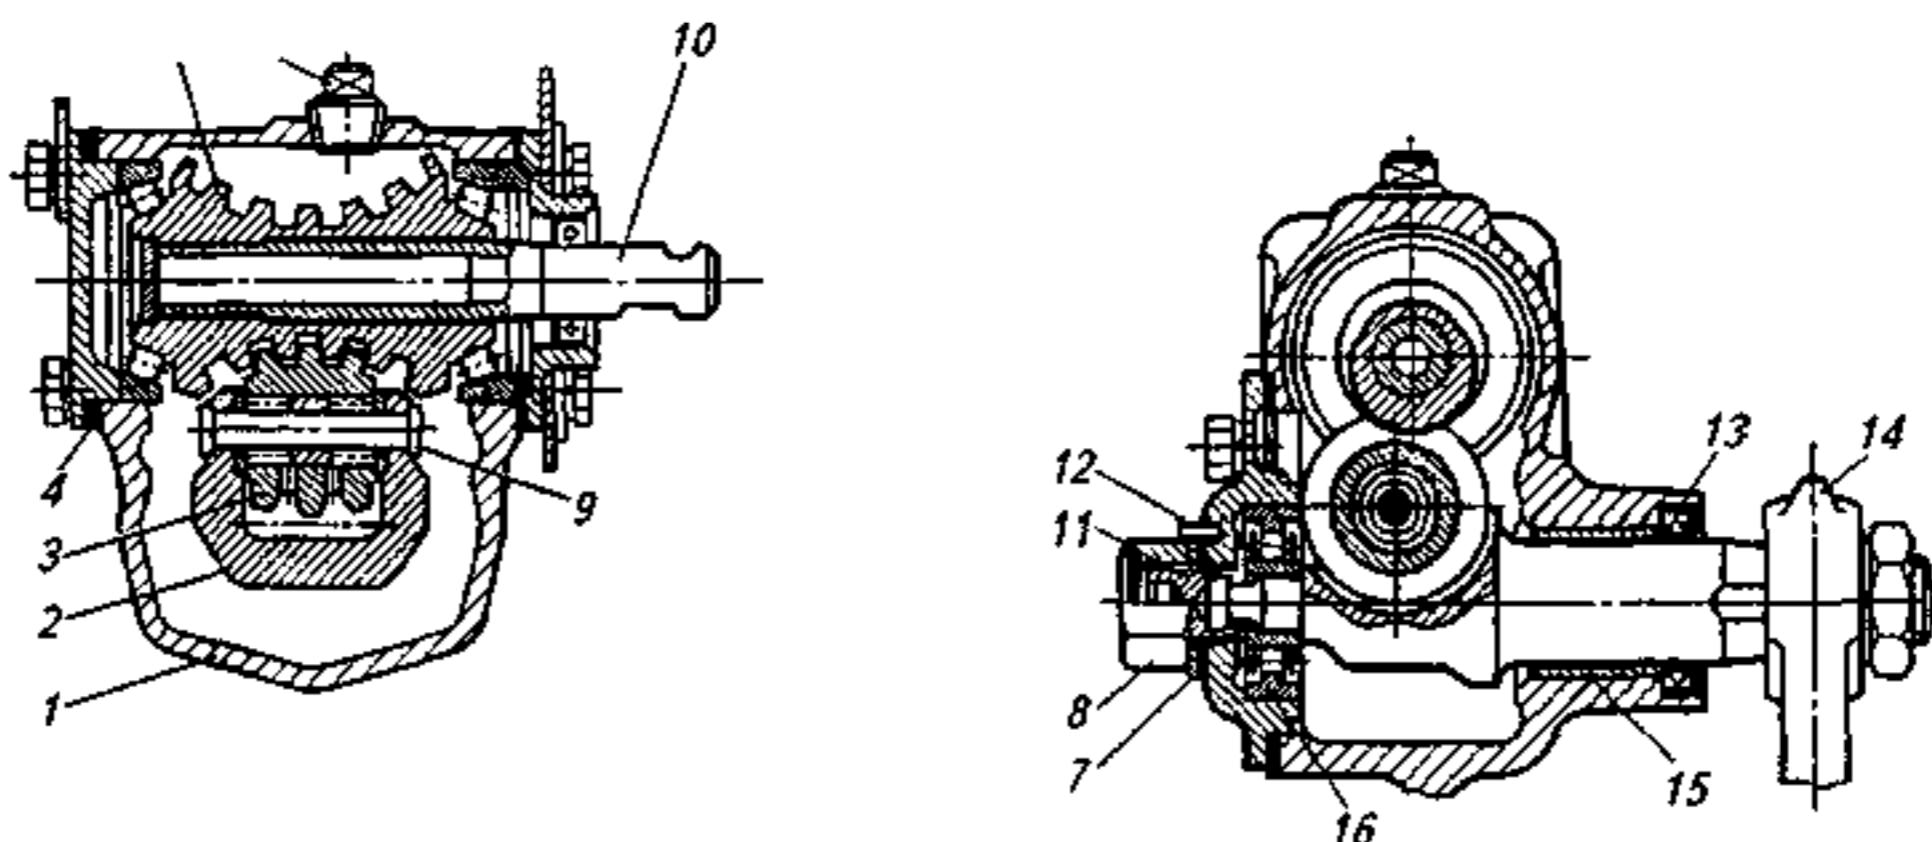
Рулевой механизм типа червяк — ролик: 1 — картер механизма; 2 — вал сошки; 3 — трехгребневый ролик; 4 — прокладка; 5 — червяк; 6 — пробка; 7 — стопорная шайба; 8 — колпачковая гайка; 9 — ось ролика; 10 — вал руля; 11 — регулировочный винт; 12 — стопорный штифт; 13 — сальник; 14 — рулевая сошка; 15 — бронзовая втулка; 16 — роликовый подшипник.
